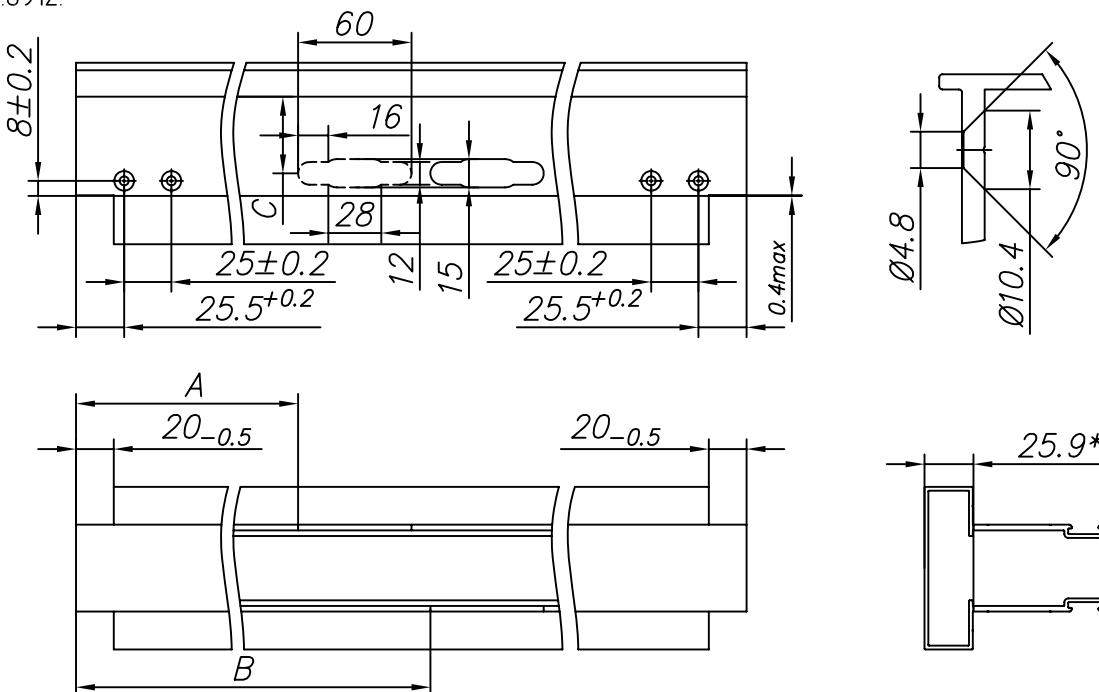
Изготовление импоста с пазами для тросовой растяжки
